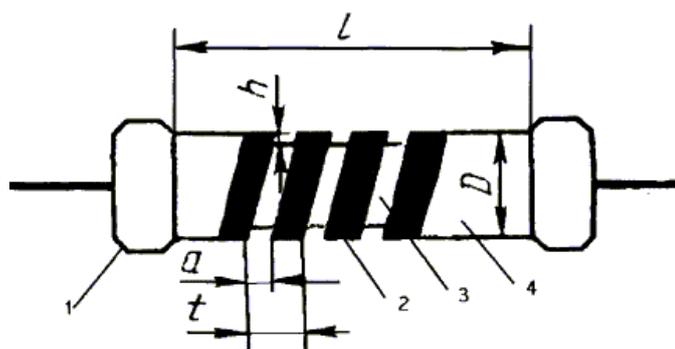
Конструкция пленочного резистора с резистивной пленкой, нанесенной на поверхность керамического цилиндра.
